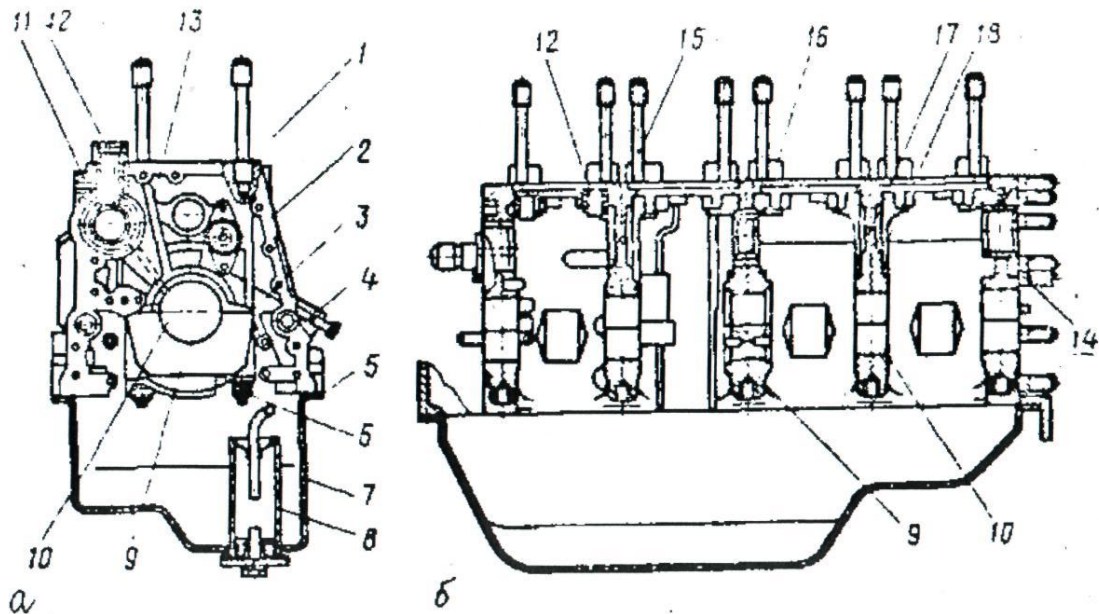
Картер однорядного чотирициліндрового двигуна:
